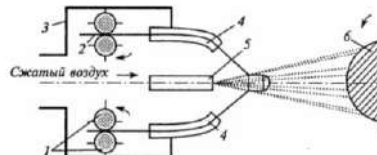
Схема дуговой металлизационной установки 1 – ролики подающие; 2 – проволока; 3 – провода электрические; 4 – направляющие; 5 – сопло; 6 – заготовка
